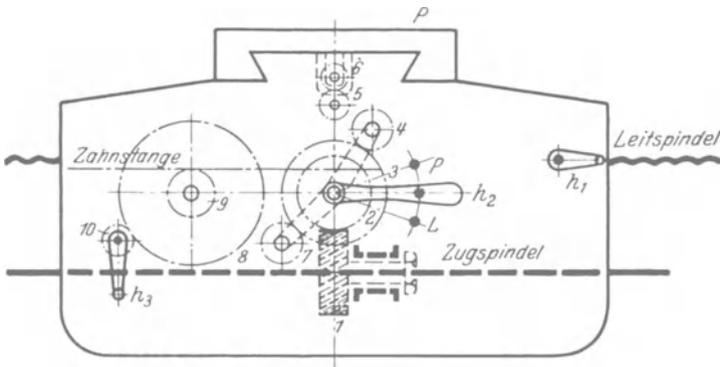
Längs- und Planzug mit 2 Schwenkrädern.
